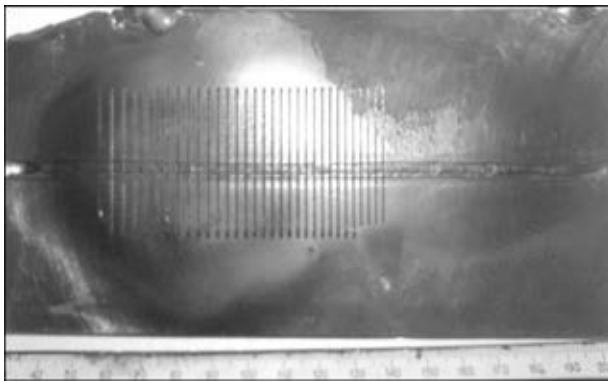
Внешний вид прямоугольной развертки, используемой для ЛТО
